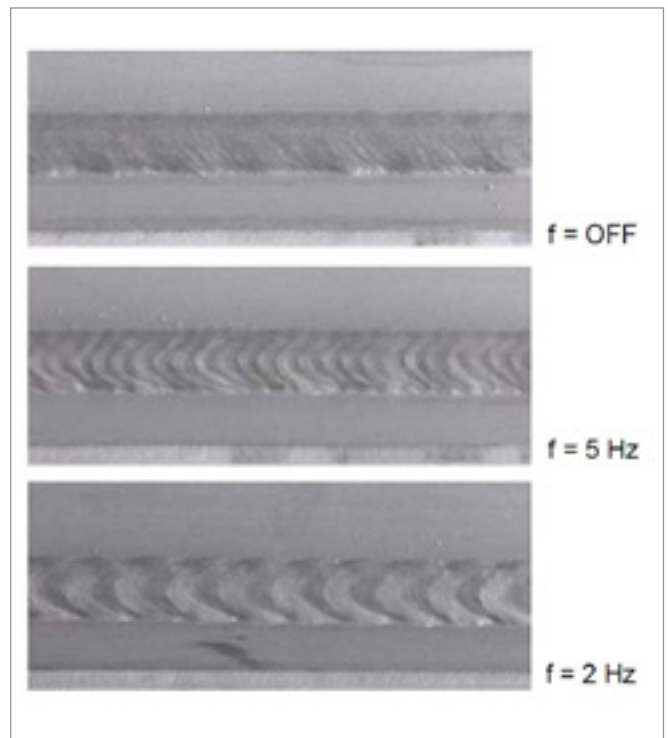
Schweißnahtoberflächen von Aluminium-Schweißnähten mit MSG-Impuls/Impuls
